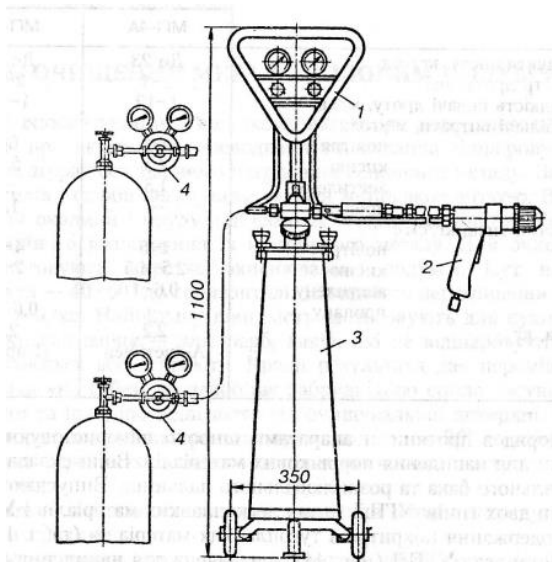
Установка УГПЛ для газопорошкового напилення :
